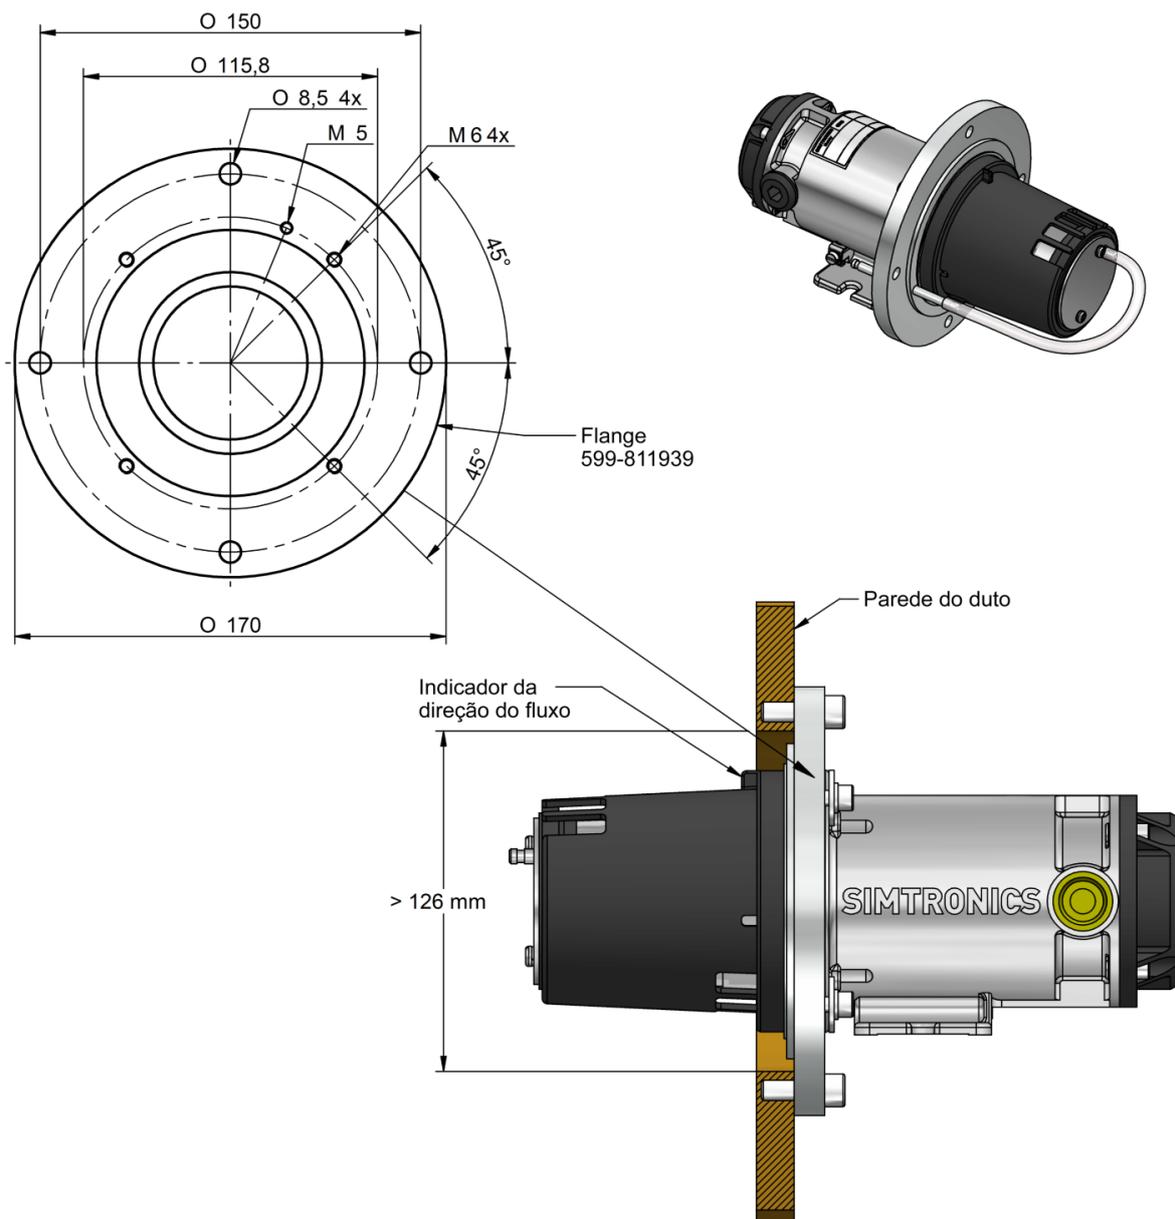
Duto de ventilação ou montagem de duto utilizando kit de flange de montagem de duto (ver Figura 3 para detalhes)
